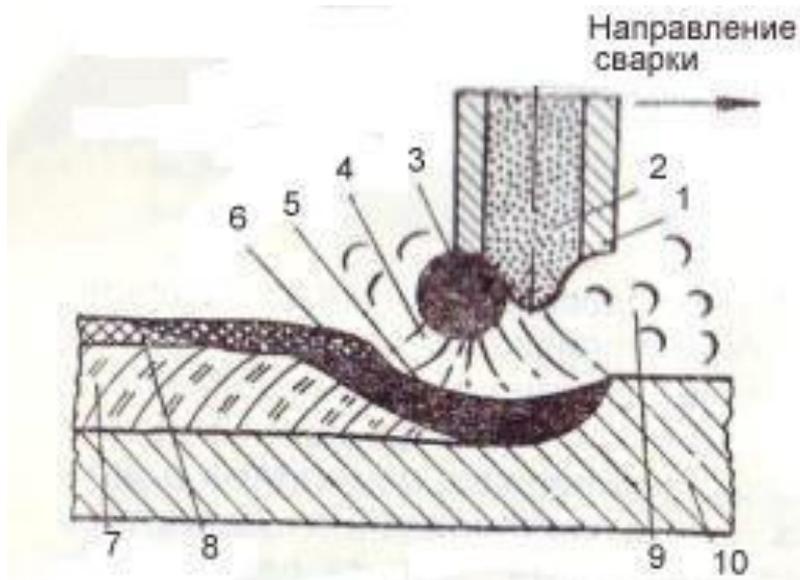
Схема процесса сварки самозащитной порошковой проволокой.
